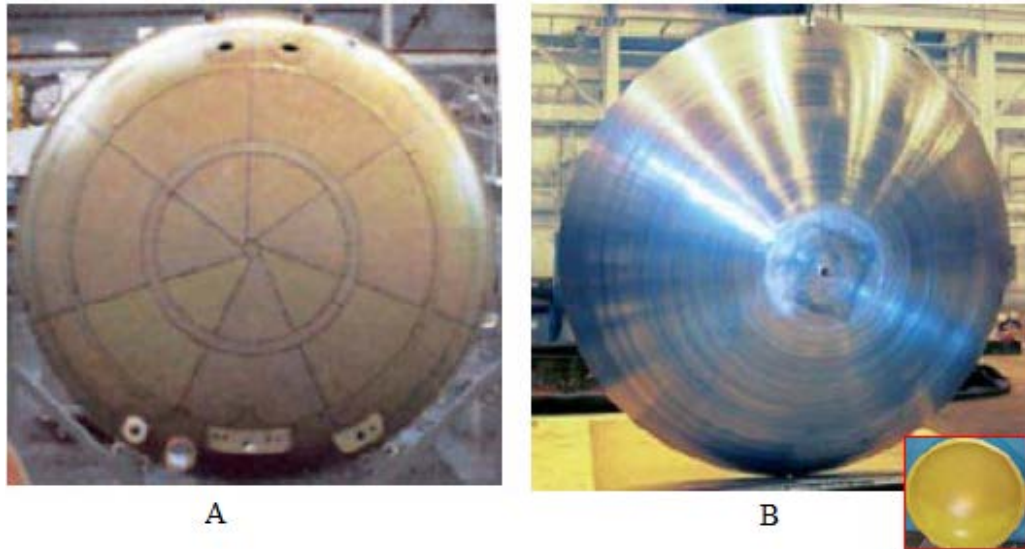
Caverna de pressão em fuselagem de aeronaves. Foto (A) componente produzido anterior ao processo FSW constituído de 60 chapas, 2500 rebites e cerca de 300m de selagem. Foto (B) componente produzido pelo processo FSW constituído diretamente por uniões das chapas soldadas de topo. Adaptado de [7].
